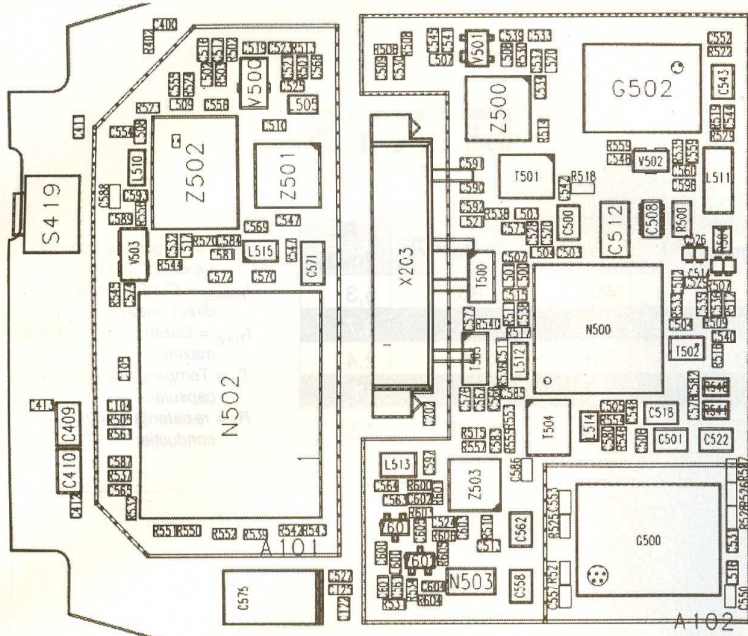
Desenul de amplasare a componentelor blocului RF pe PCB
